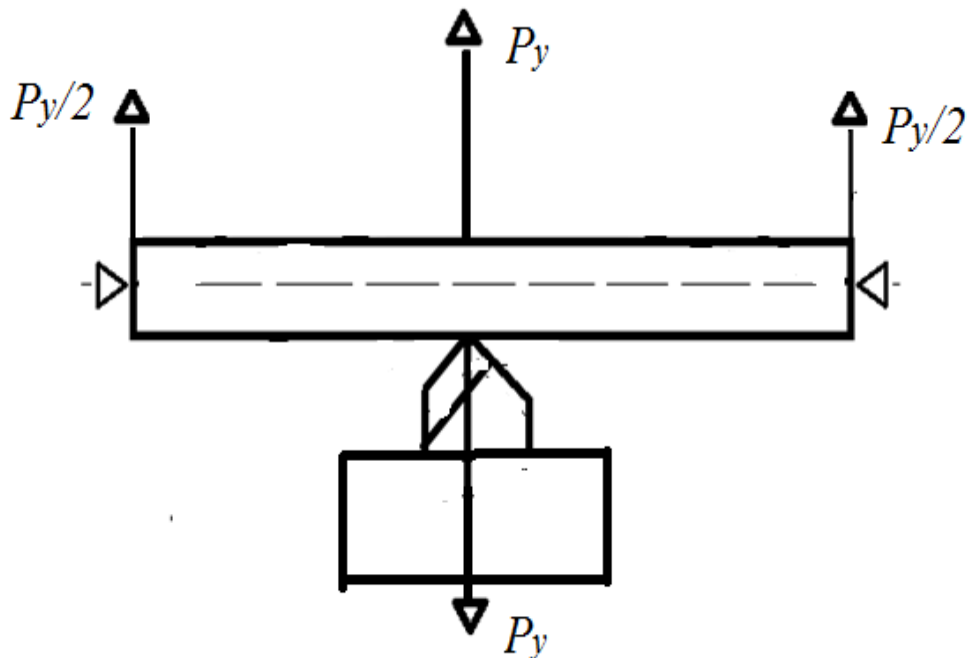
Картина зусиль при токарному обробленні у центрах
